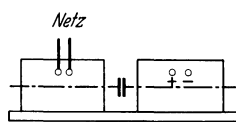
Gleichstrommotor gekuppelt mit Schweißmaschine.
